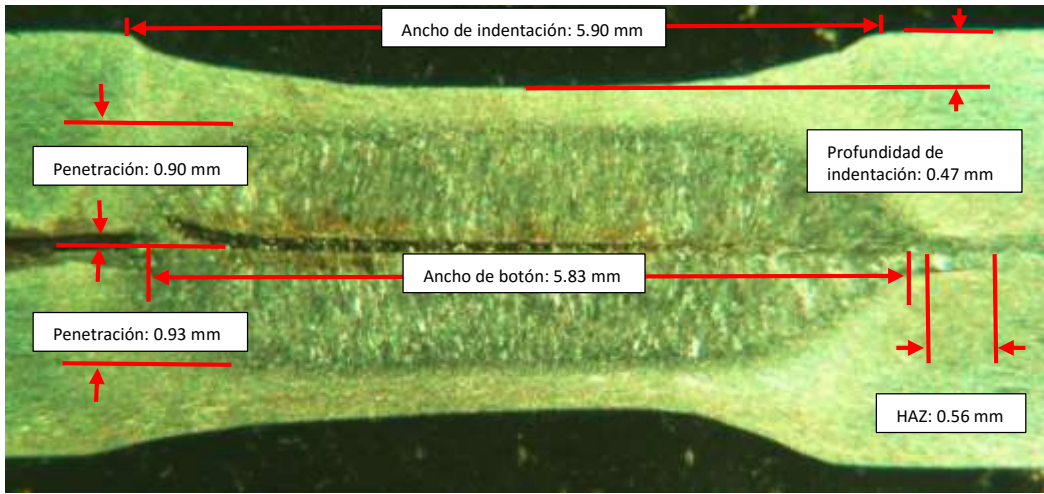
Mediciones realizadas en el botón de soldadura número 15.
